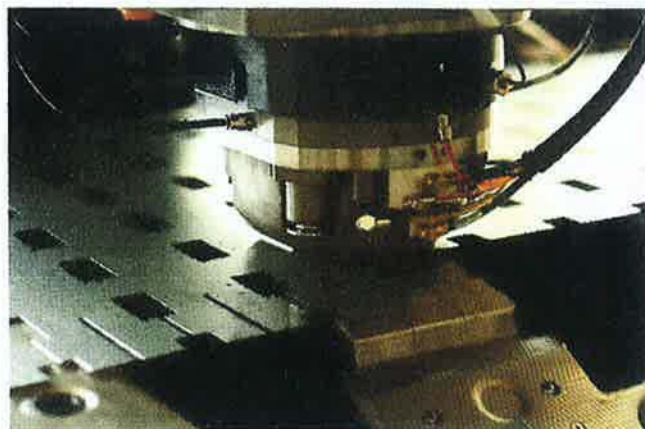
Mecanizado mediante punzonado de chapa galvanizada con matriz en forma rectangular.
